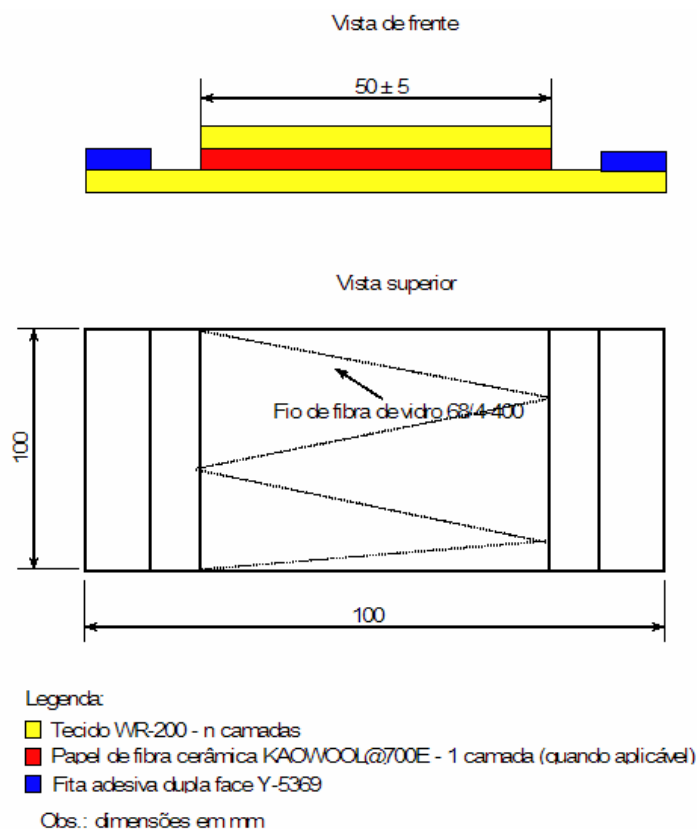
Desenho esquemático com as vistas frontal e superior com dimensões dos modelos de suportes de solda à base de fibra de vidro
